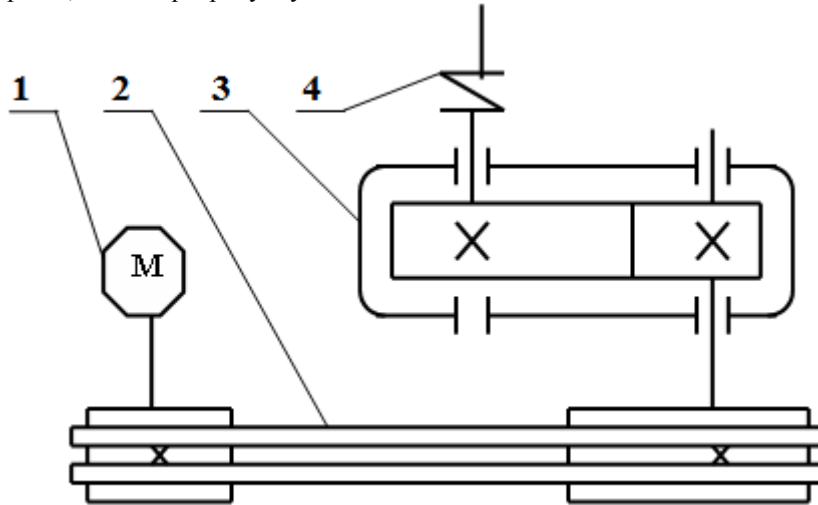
Привод стрічкового конвеєра: 1 – електричний двигун, 2 – пасова передача, 3 – одноступінчатий прямозубий циліндричний редуктор, 4 – муфта типу МПВП.
